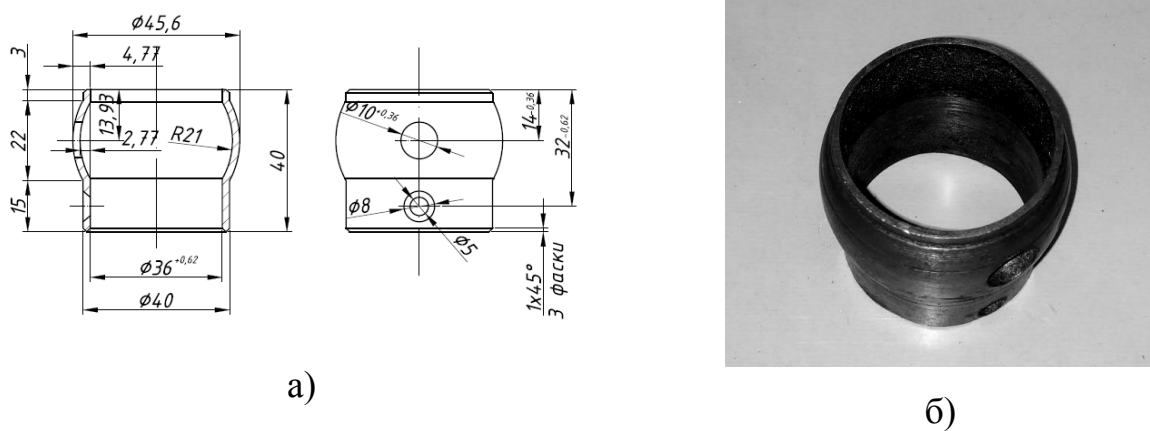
Сферична втулка (корпус) а) конструктивна схема;
